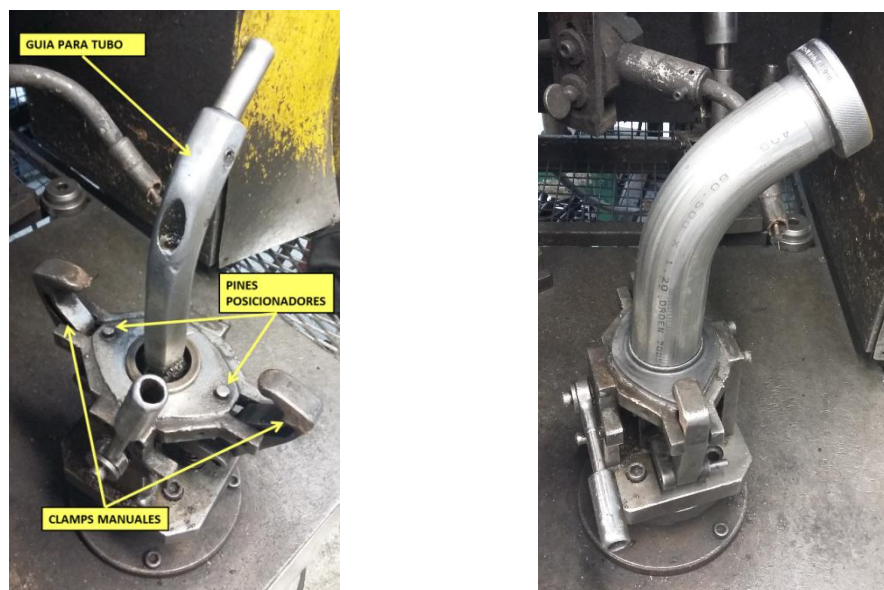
DISPOSITIVO DE SOLDADURA MÁQUINA MESA GIRATORIA
